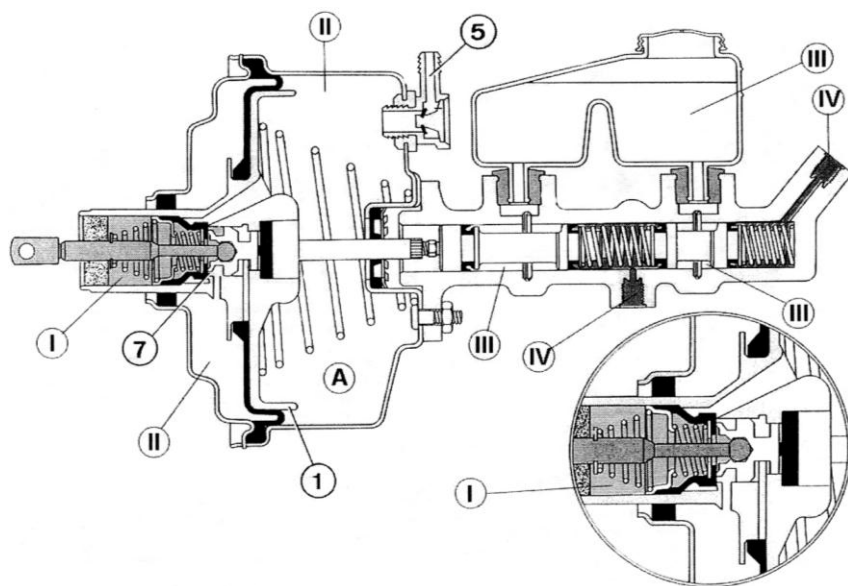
Положение деталей вакуумного усилителя конструкции «mastervac» при частично нажатой педали тормоза
